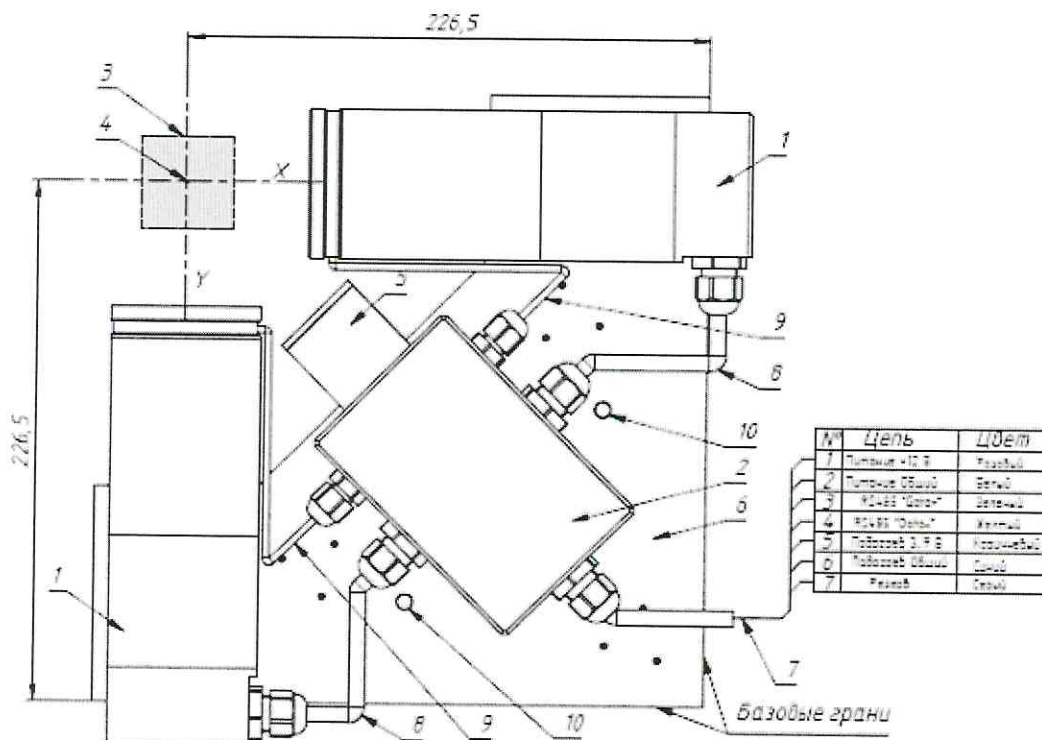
Общий вид измерителя (ФПКС-2М-40, ИКСО-40), вид сверху
